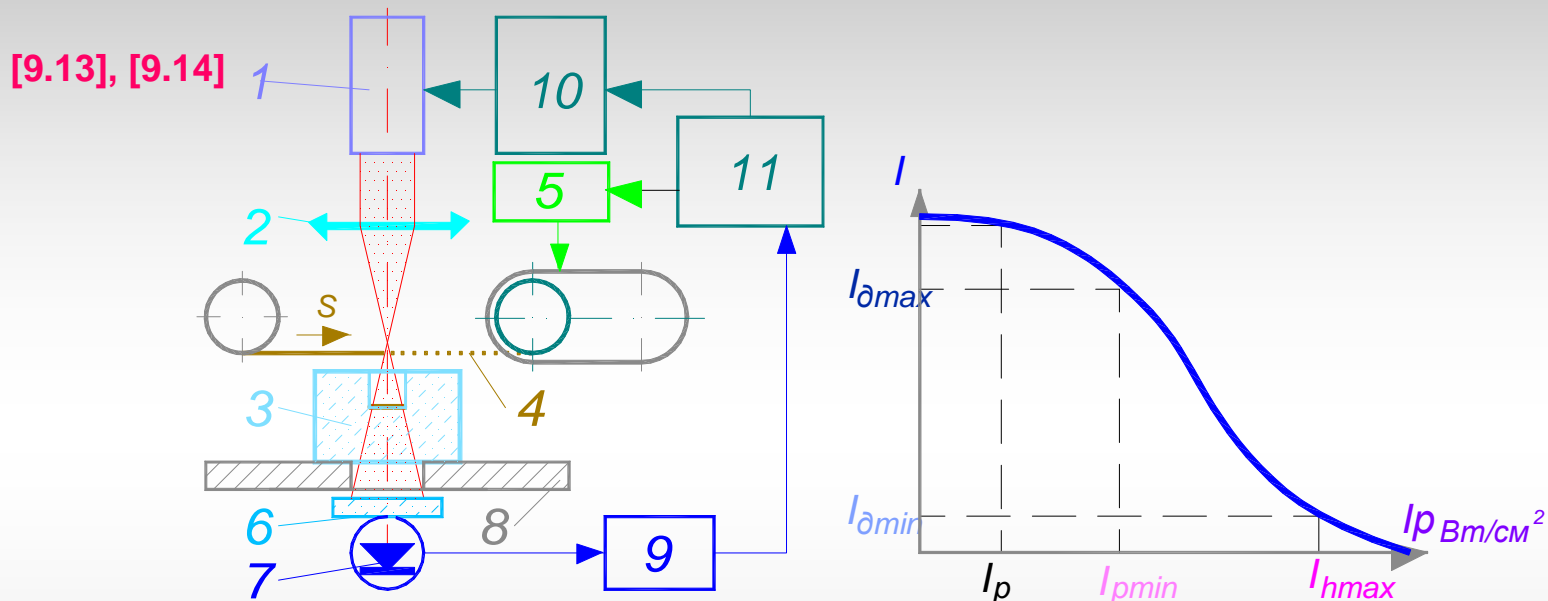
(13.10). Пристрій для обробки глибоких отворів в заготовках із прозорих матеріалах
